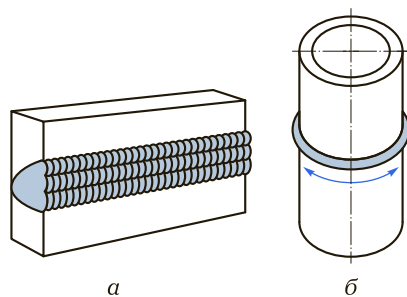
Положение при сварке стыковых швов:
